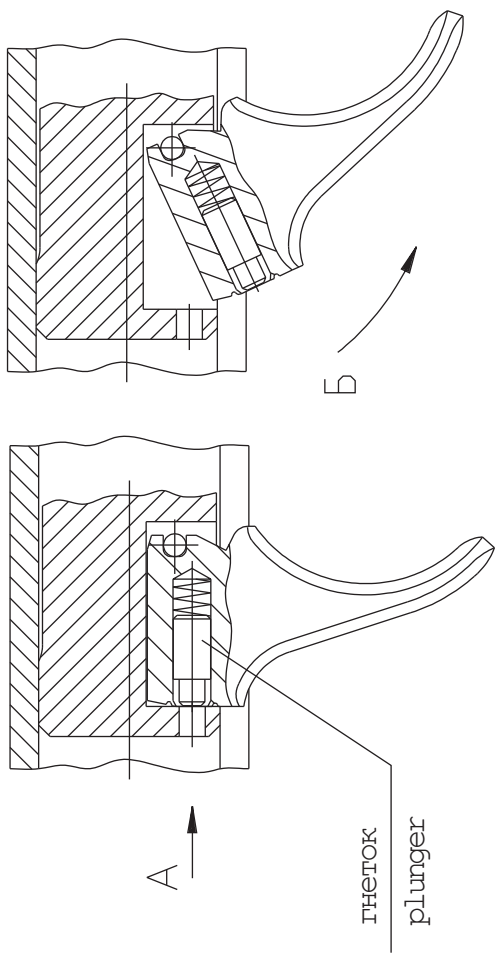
Схема разборки затвора с рукояткой.
